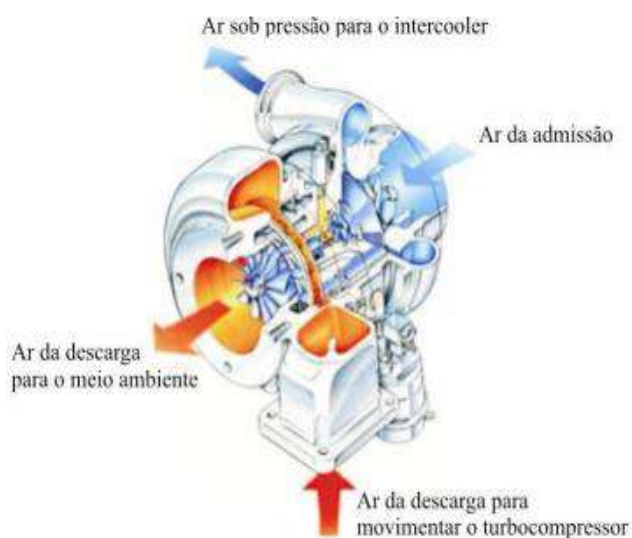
turbocompressor, turbo alimentador, turbina ou turbo.
